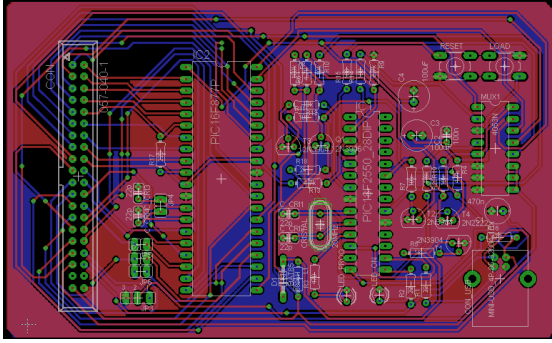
Diseño de la PCB de la tarjeta microcontrolador de prueba y hardware de programación.
